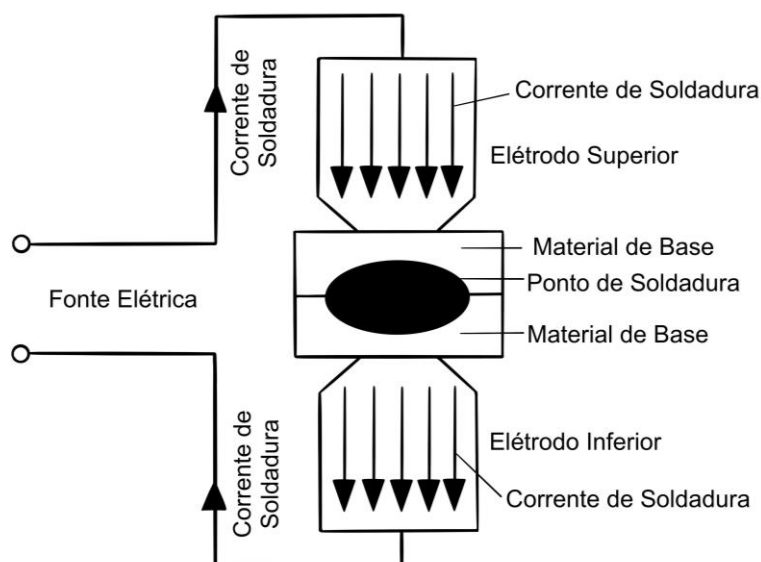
Diagrama representativo do processo de RSW (*Resistance Spot Welding*). Adaptado de [3]
